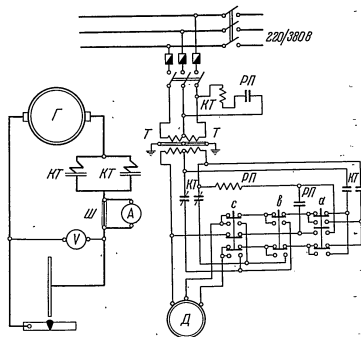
Принципиальная электрическая схема сварочного трактора ТС-17-М для сварки на постоянном токе:
